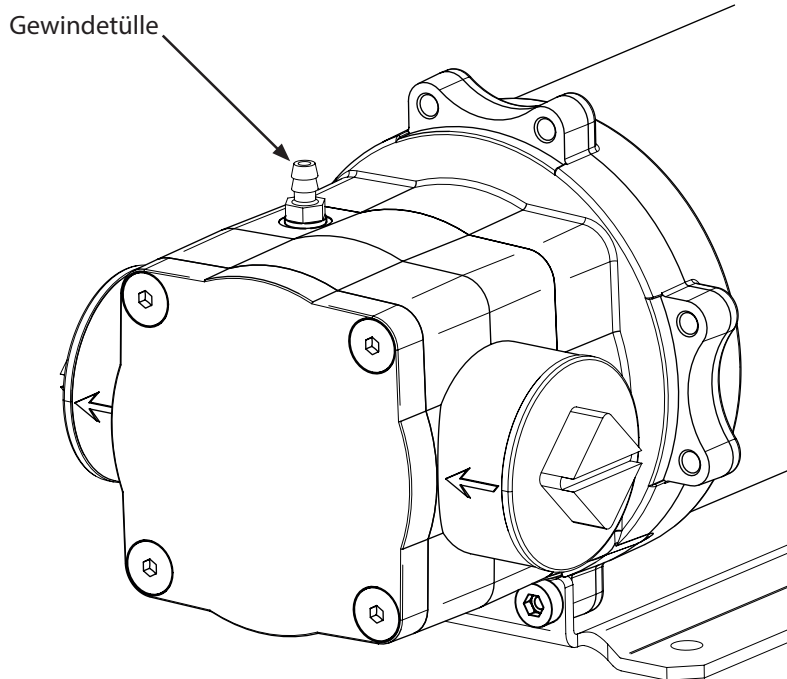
Gewindetülle für Heberschutz eingeschraubt
